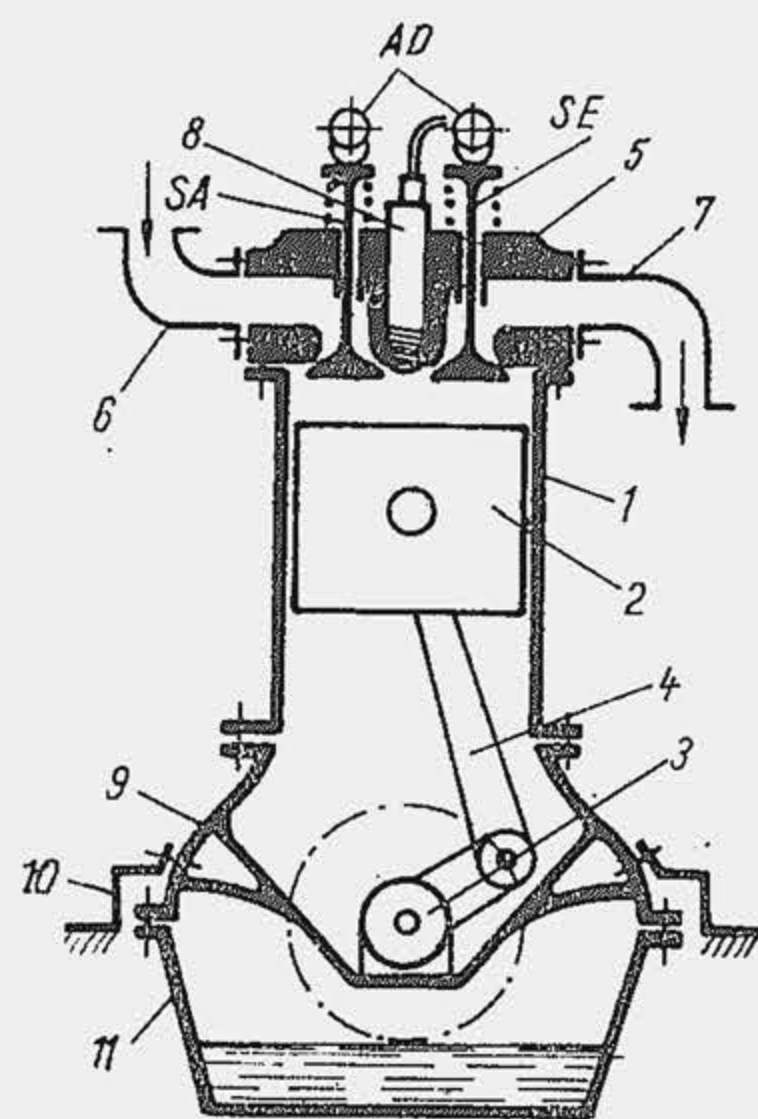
Schema de principiu a unui motor în patru timpi cu un cilindru.
